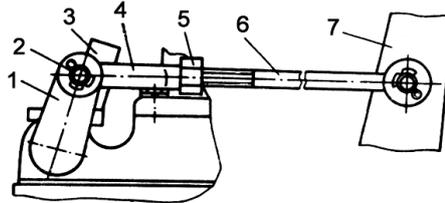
Схема регулировки привода насоса гидравлической системы коробки передач
